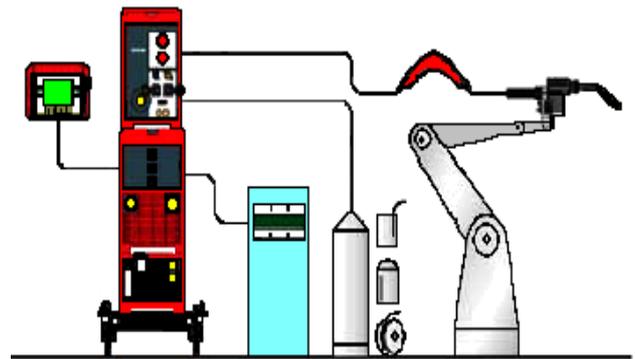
Esquema del proceso de soldadura de transferencia de metal en frío. [10]
